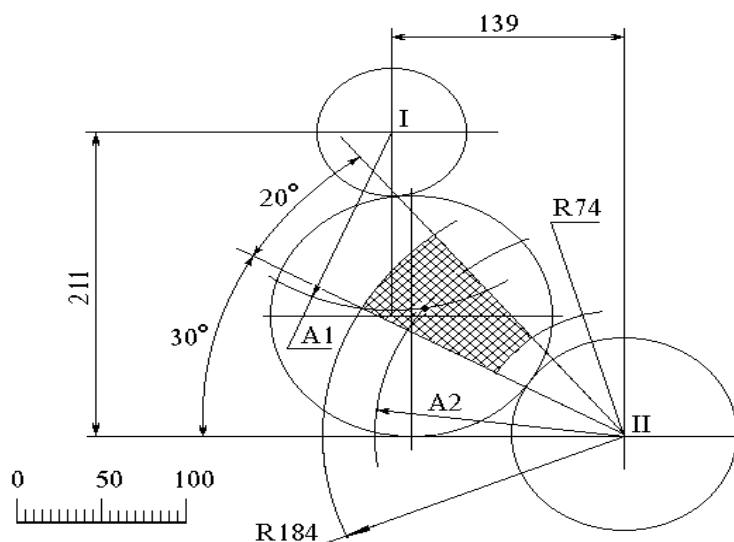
Чертеж для проверки возможности сцепления сменных шестерен
